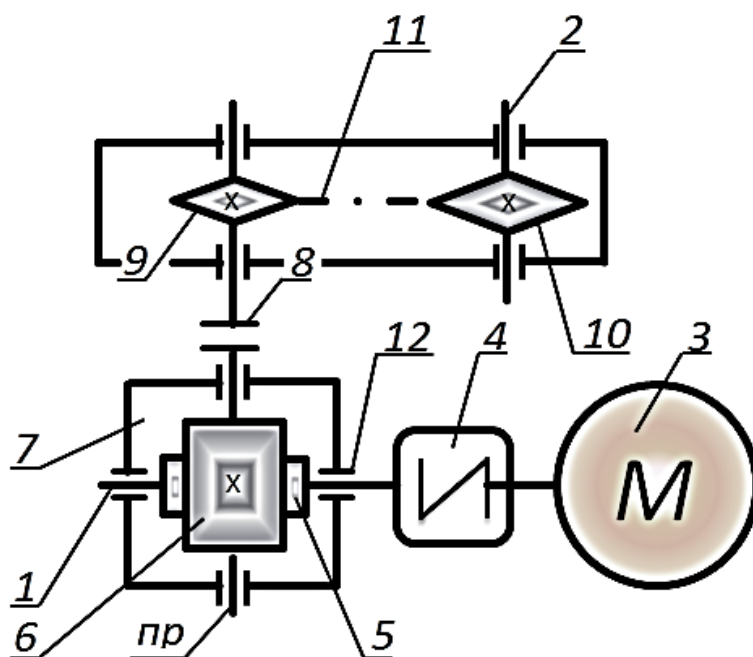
Схема привода с червячным редуктором и закрытой цепной передачей:
